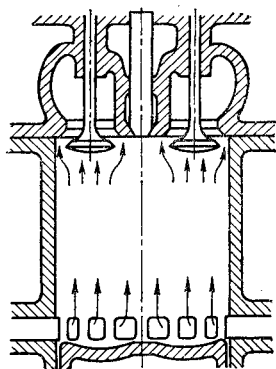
Цилиндр двигателя с клапанно-щелевой схемой газообмена
